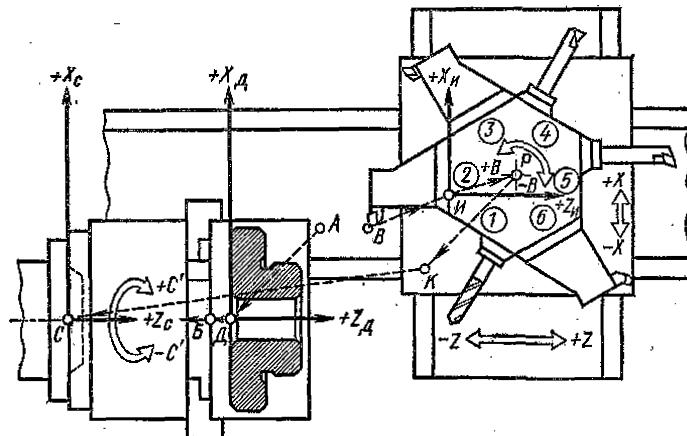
Связь систем координат детали, станка и инструмента при токарной обработке
